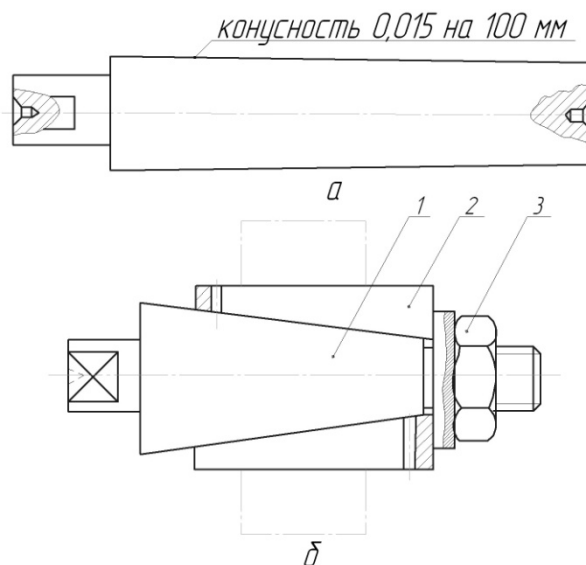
Оправки для установки заготовок по отверстиям: а - коническая; б – с разжимной разрезной втулкой
